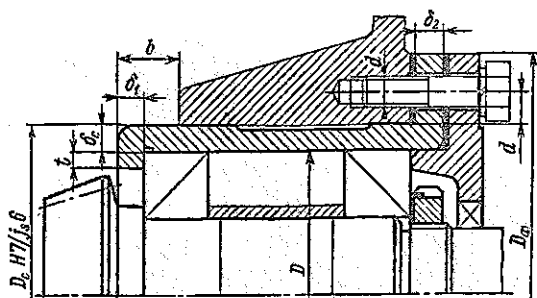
Конструкция стакана для фиксирующих опор или опор конических зубчатых колес
